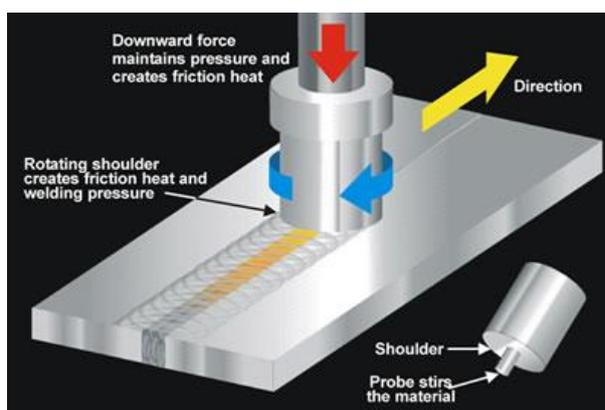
Schéma de principe du Friction Stir Welding (ESAB).
